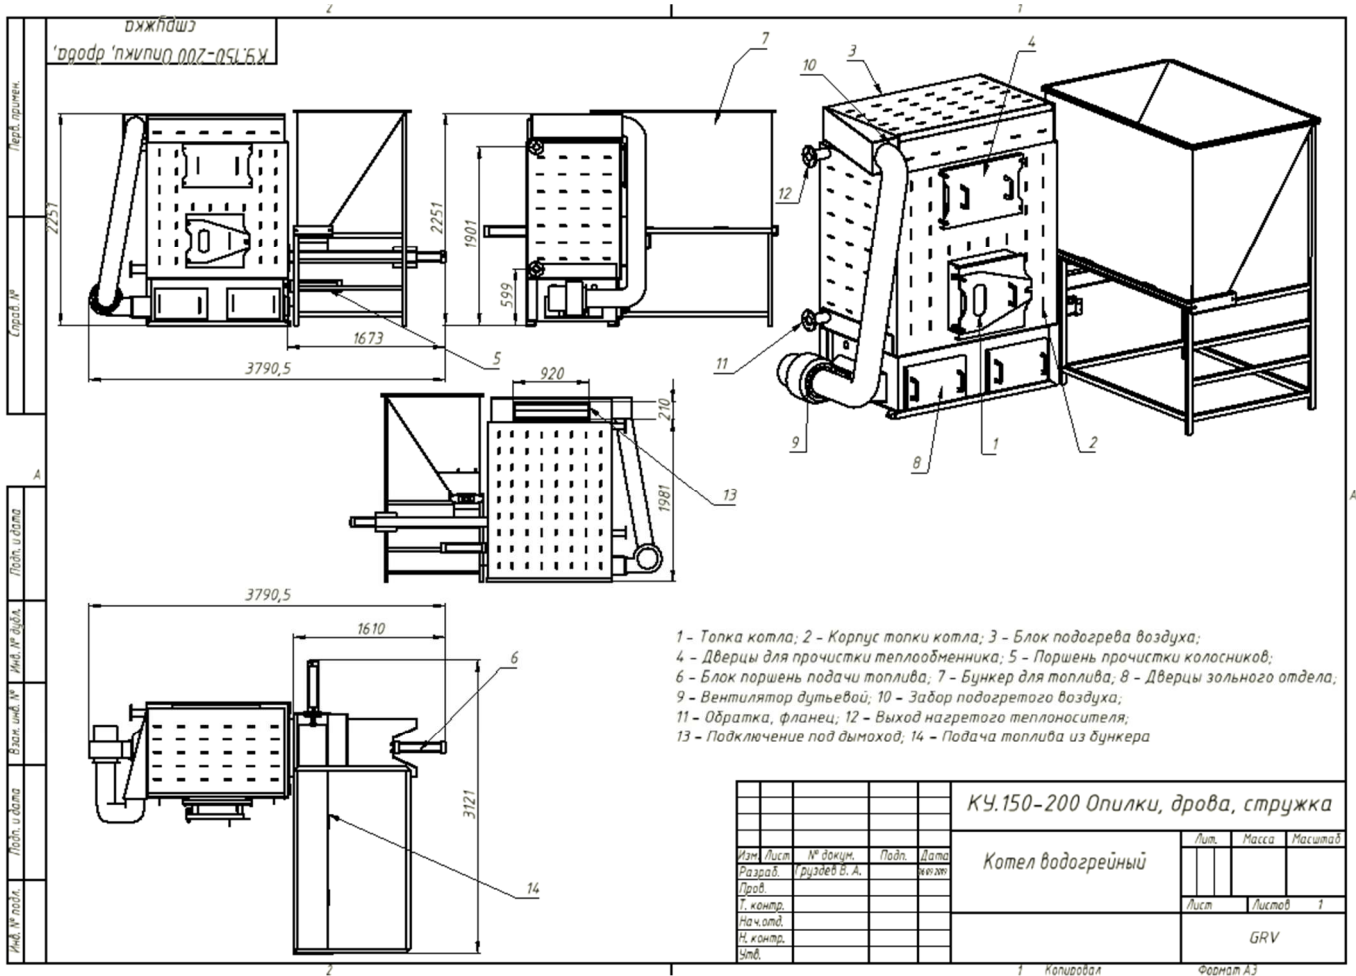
Чертеж котла. 1 – Топка котла; 2 – Корпус топки котла; 3 – Блок подогрева воздуха; 4 – Дверцы для прочистки теплообменника; 5 – Поршень прочистки колосников; 6 – Блок поршень подачи топлива; 7 – Бункер для топлива; 8 – Дверцы зольного отдела; 9 – Вентилятор дутьевой; 10 – Забор подогретого воздуха; 11 – Обратка, фланец; 12 – Выход нагретого теплоносителя; 13 – Подключение под дымоход; 14 – Подача топлива из бункера
